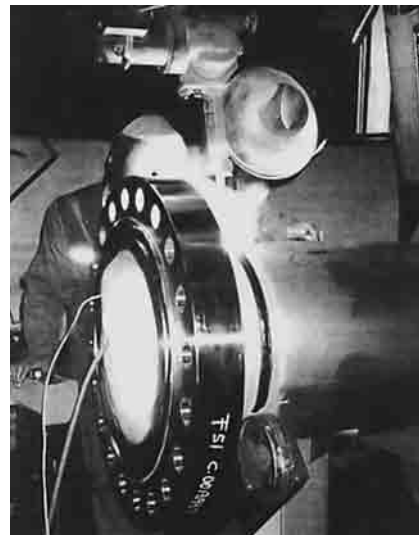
Сварное соединение трубы и фланца из стали 1.4462 (UNS 31803), сваренное порошковой проволокой CN 22/9 N-FD диаметром 1,2 мм (завод Visser Smith Hanab, Нидерланды)
